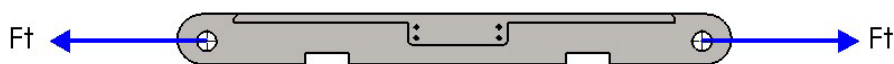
Viga horizontal sometida a tracción (Fuente: propia)
